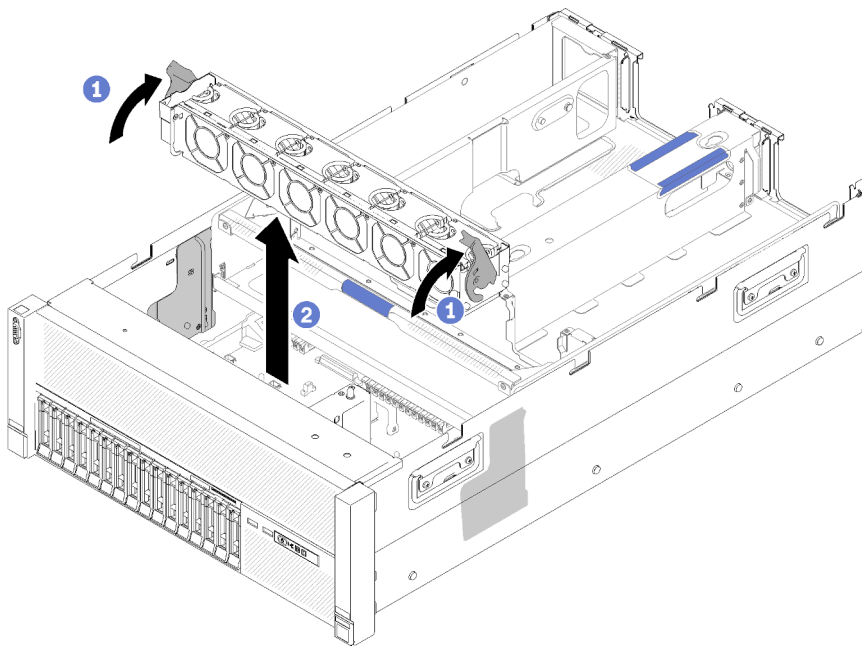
Entfernen der Lüfterrahmenbaugruppe
